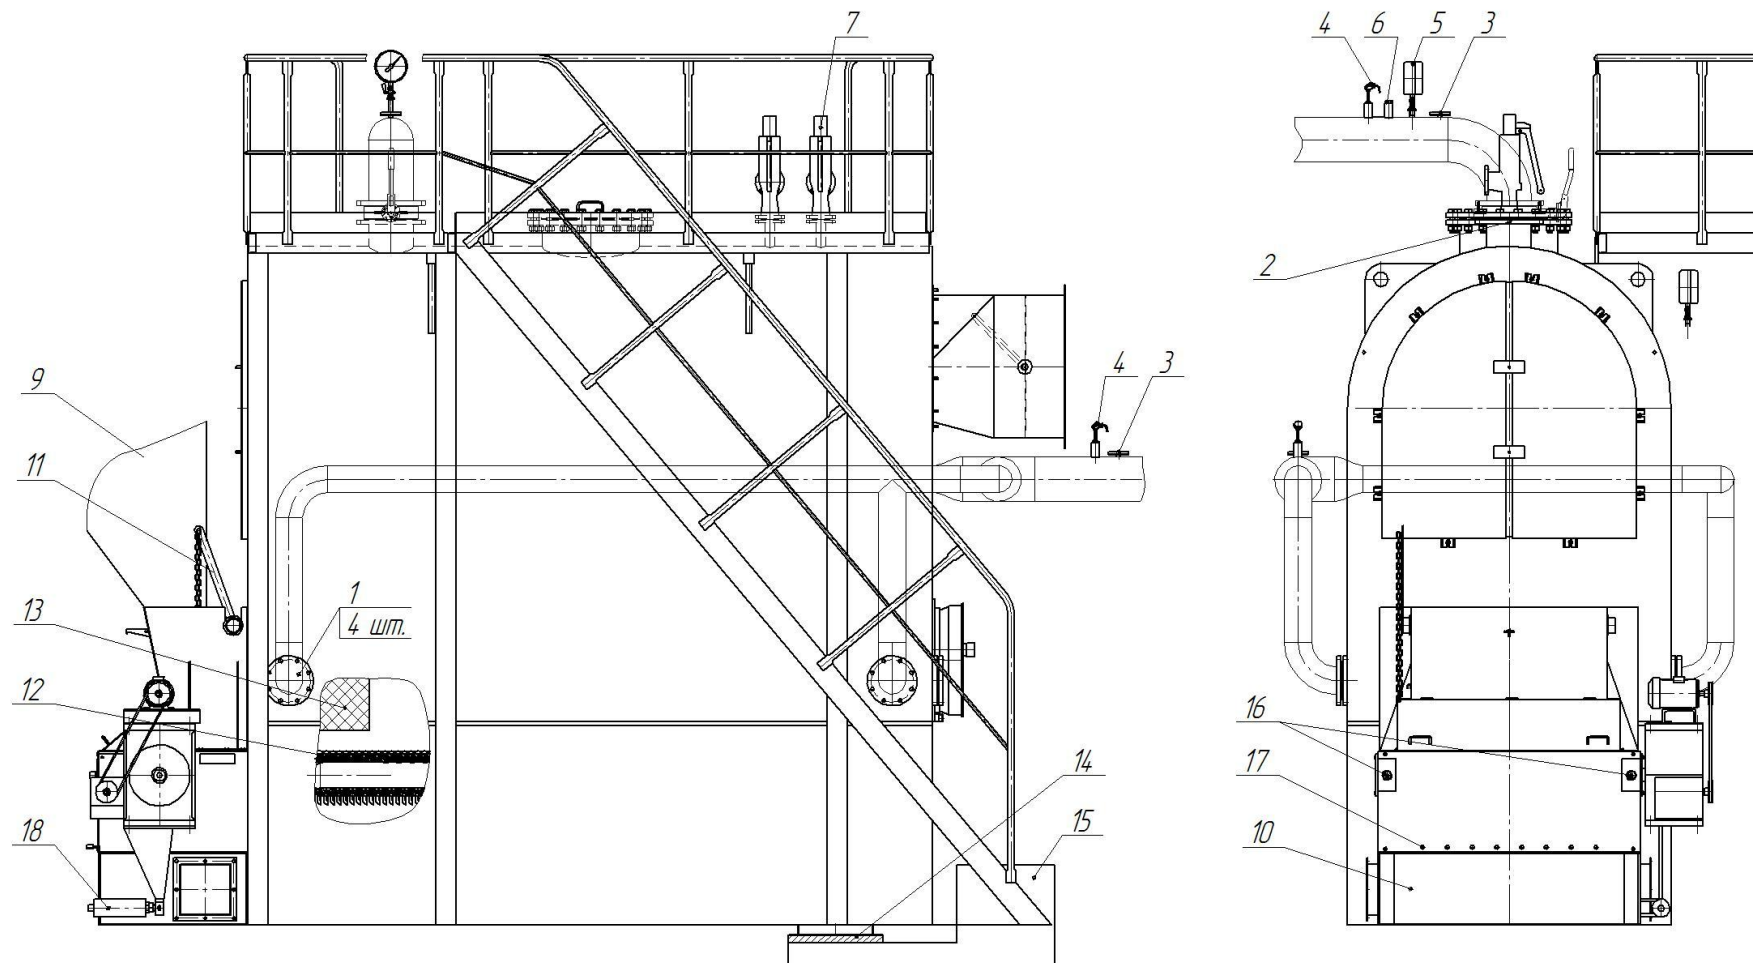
Общий вид КСВа-2.9 Р (Э)
